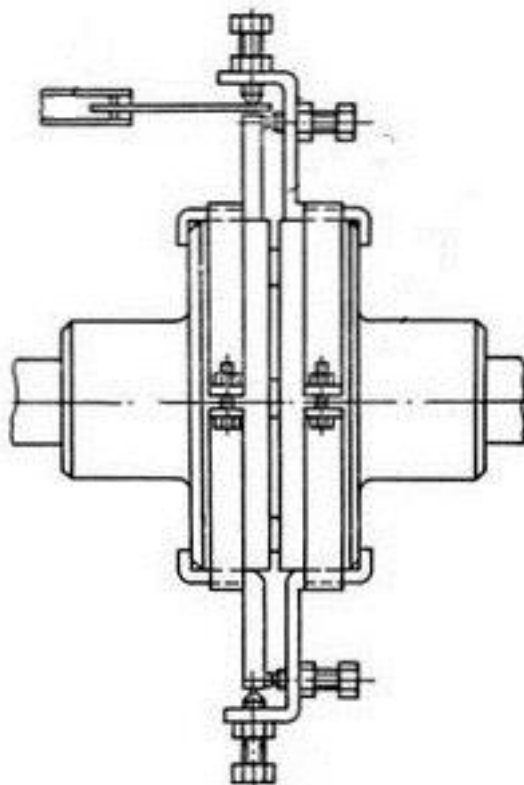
Устройство для центровки валов с зубчатыми муфтами
